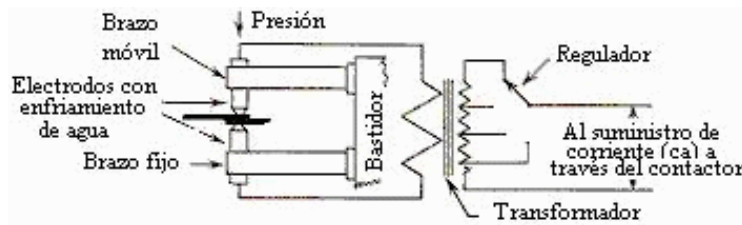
Diagrama de una máquina soldadora por puntos
